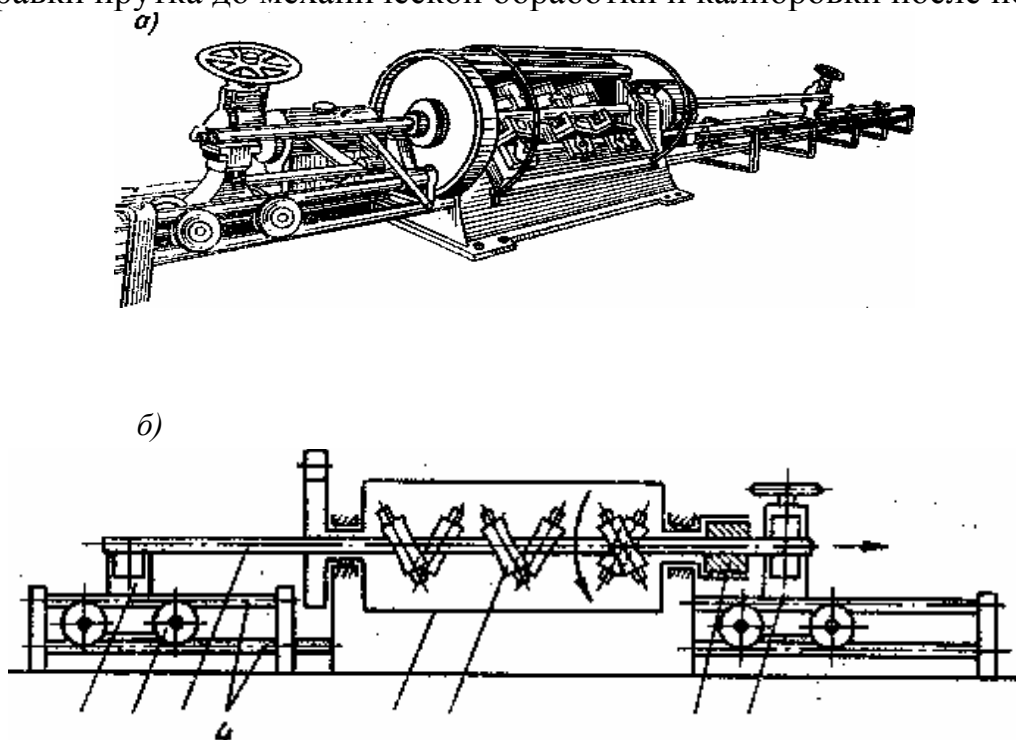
Правильно-калибровочный станок (а) и схема его работы (б)
